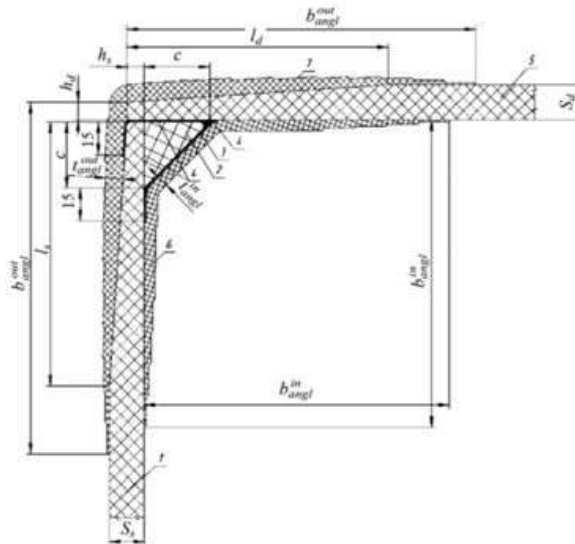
Вузол з'єднання одношарових конструкцій борту і верхньої палуби змінної товщини з установкою опорного елемента: 1 - борт; 2 - опорний елемент; 3 - обформовка опорного елемента; 4 – адгезійна речовина;
